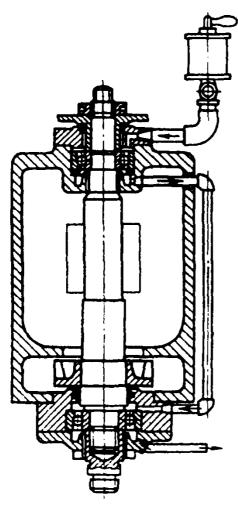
Смазка подшипников вертикального вала с помощью масленки с запорной иглой
